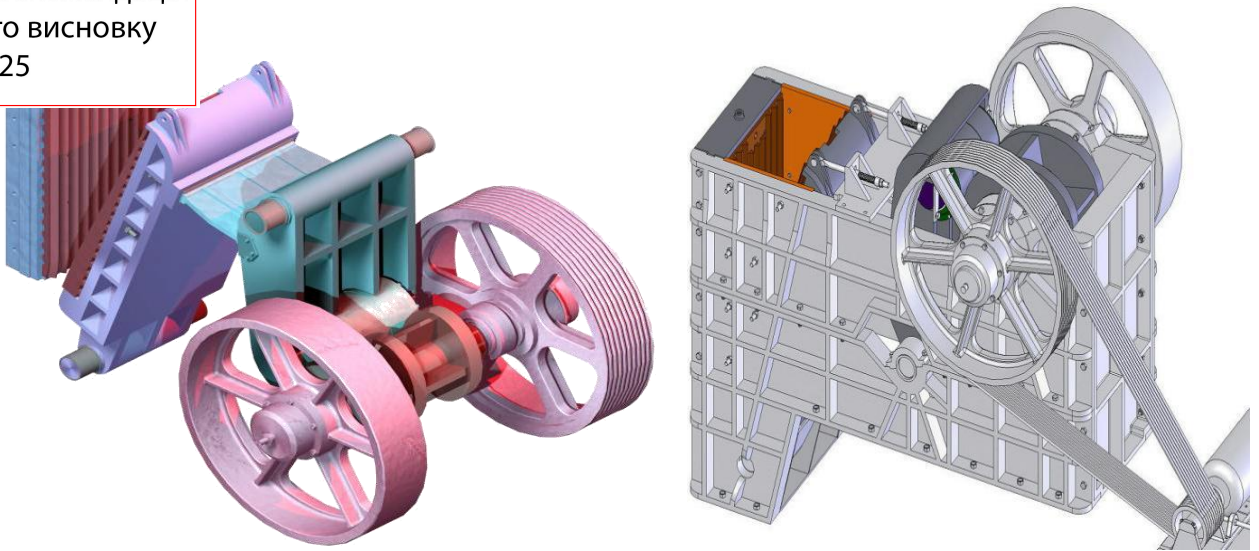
Загальний вигляд щоквої дробарки с кулачковим приводом
